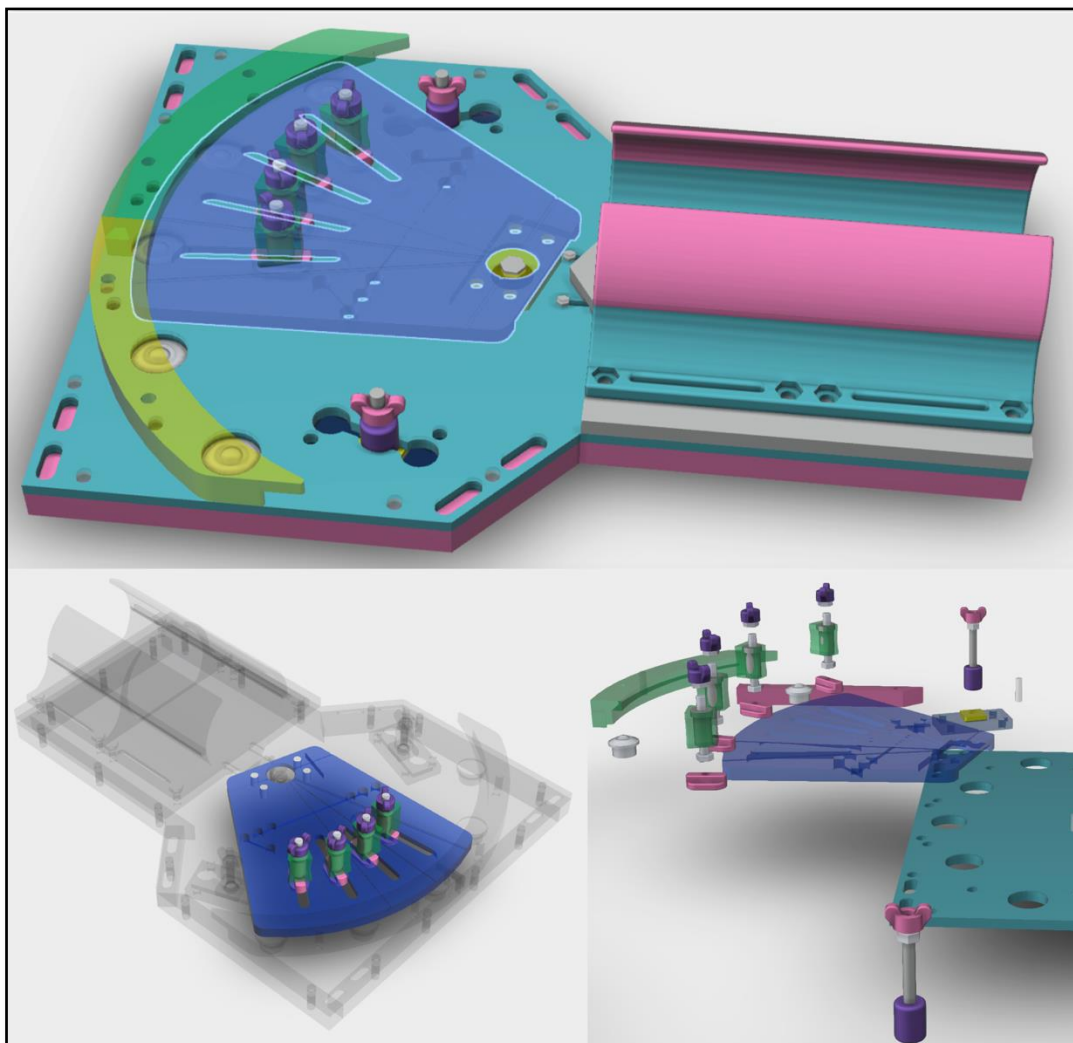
Vues 3D de la partie mobile ou amovible du dispositif GWMD.
